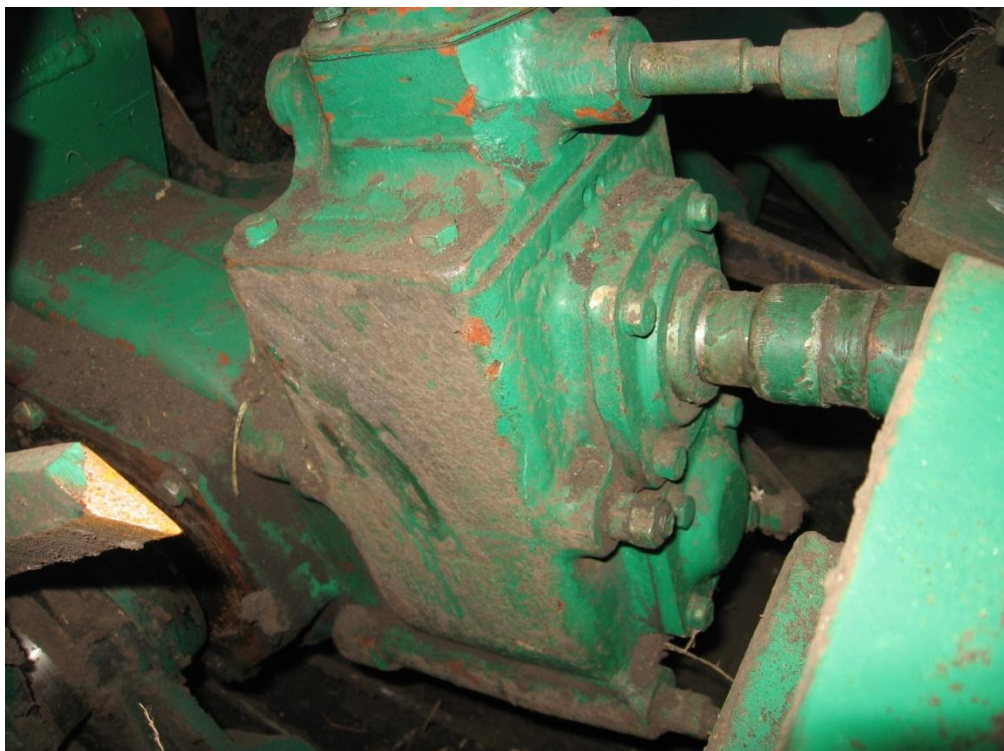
Конічно-циліндровий двоступеневий редуктор
